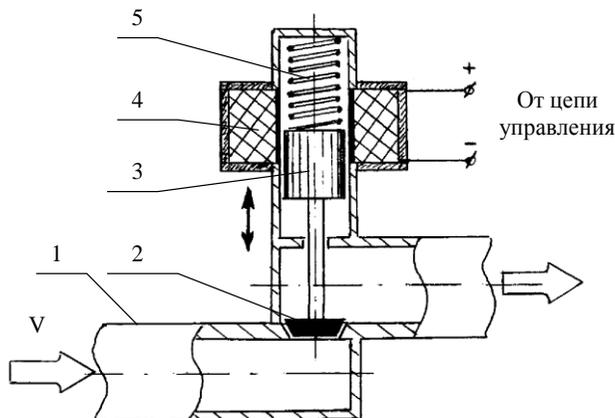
Электромагнитный клапан: 1-трубопровод; 2-клапан; 3-подвижный сердечник; 4-соленоид; 5-пружина.
